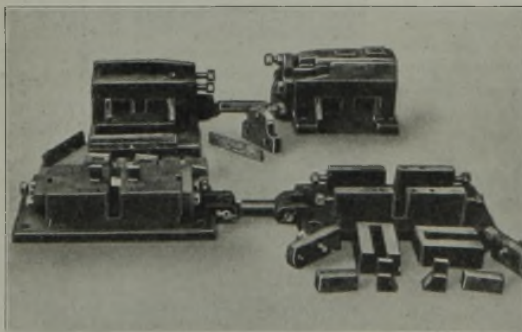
Stempel- und Matrizenhalter für die Lochwerkzeuge.
